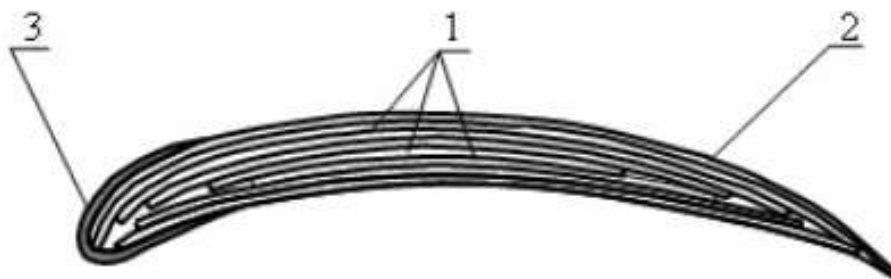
Конструкція з'єднання пера лопатки із ПКМ із полками
